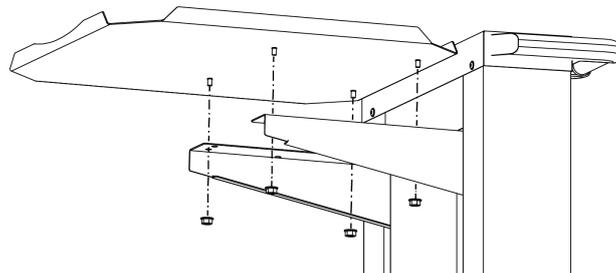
Montage de la plateforme pour paniers ou plateaux
